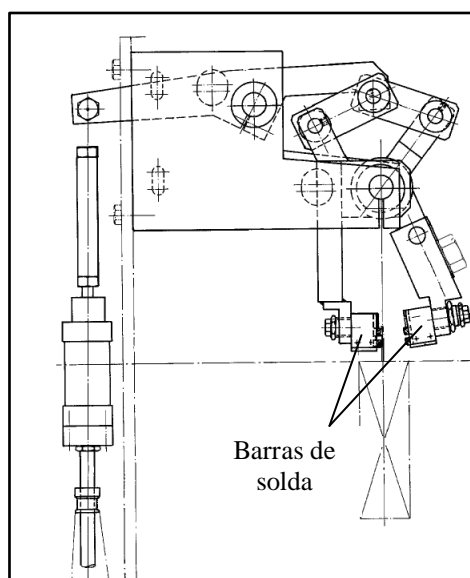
Esquema do sistema de solda térmica (empresa Bosch, 2011)
